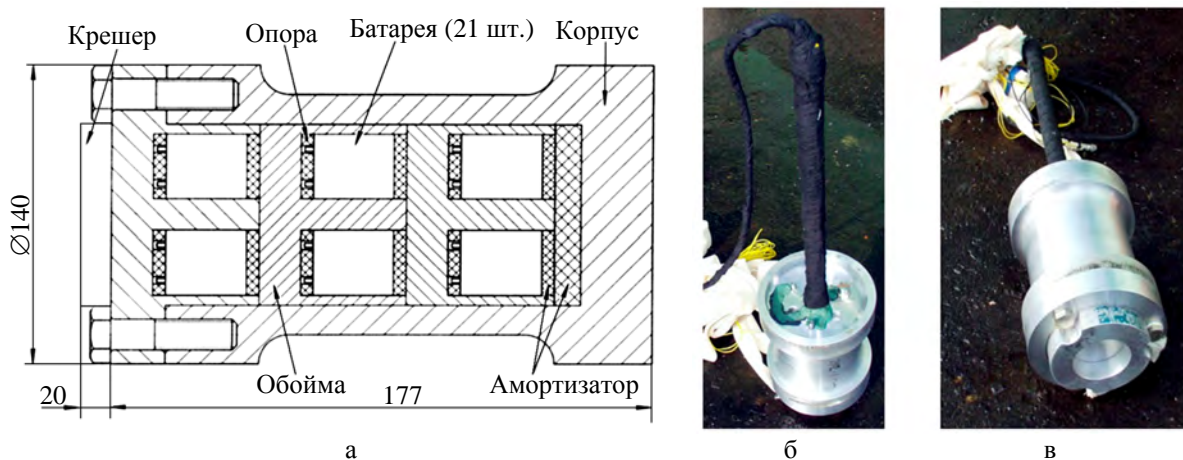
Схема (а) и внешний вид (б, в) испытательной сборки
